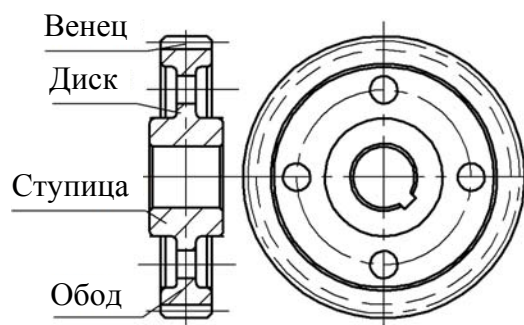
Конструкция цилиндрического зубчатого колеса
